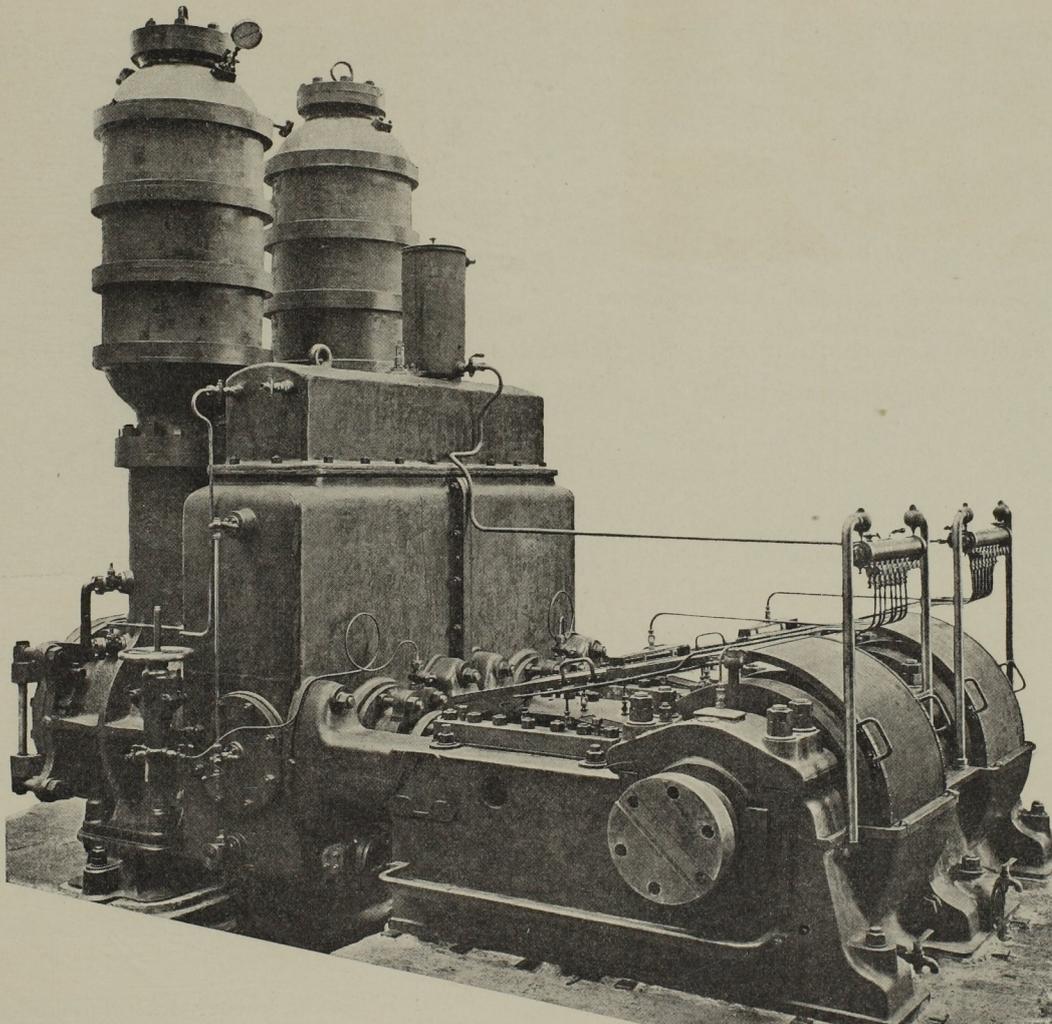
Seitenansicht der Pumpe. Triebwerksseite.
